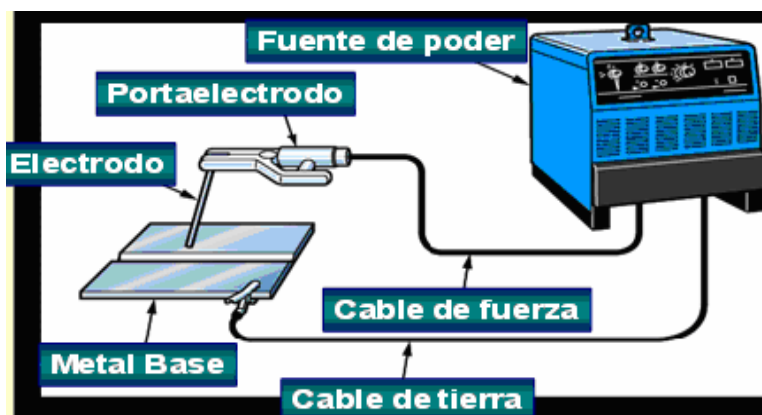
Diagrama de Equipo Básico de Soldadura (5).
